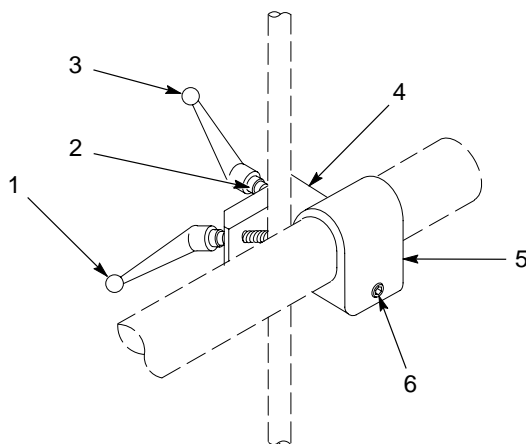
Conjunto rotativo de barra de pistola, para pistolas com tubo de suporte
